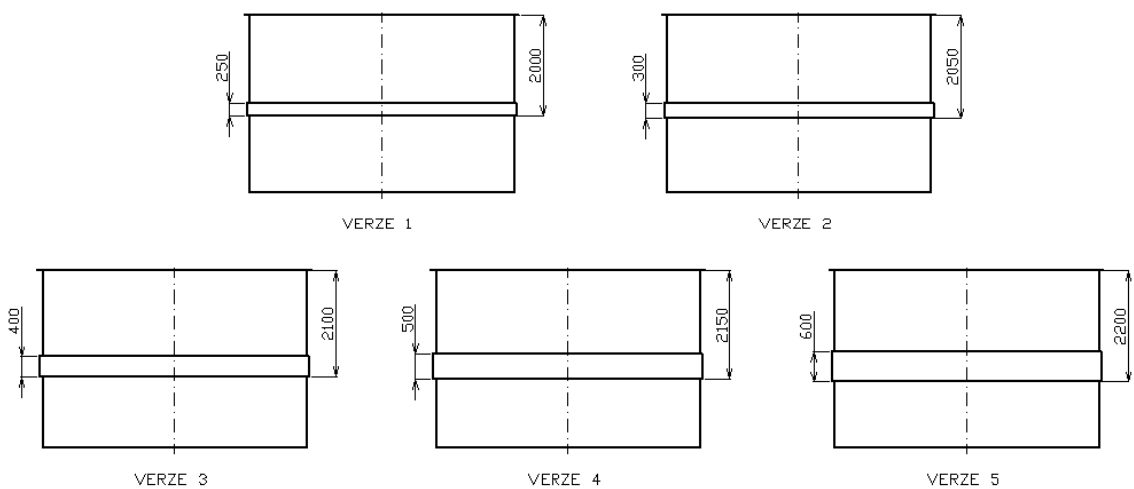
Rozmístění pásů pro základní tloušťku stěny 30 mm
